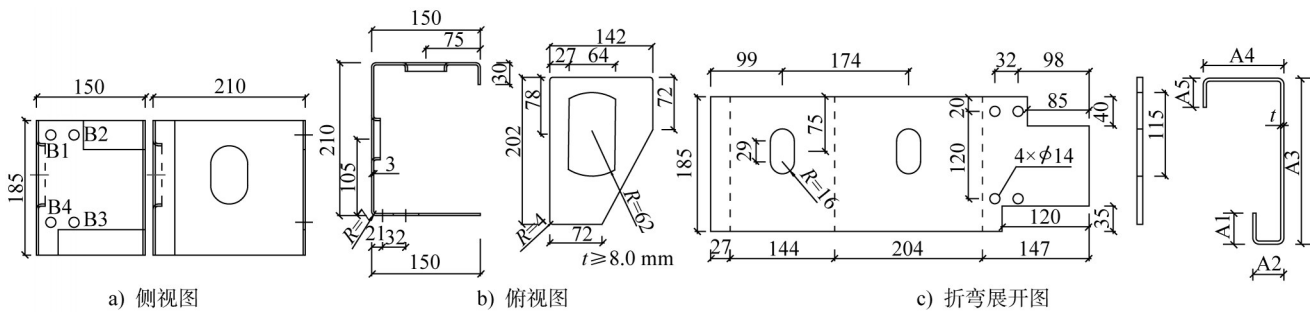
顶框角件、长边主梁截面几何尺寸(单位:mm)
